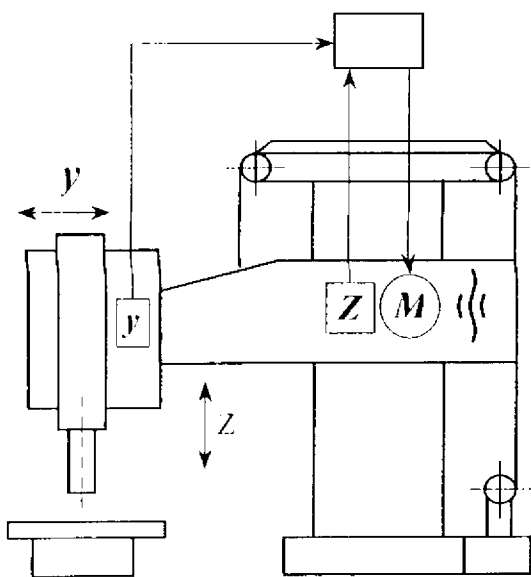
Конструктивная компенсация прогибов для координатно-расточного станка
